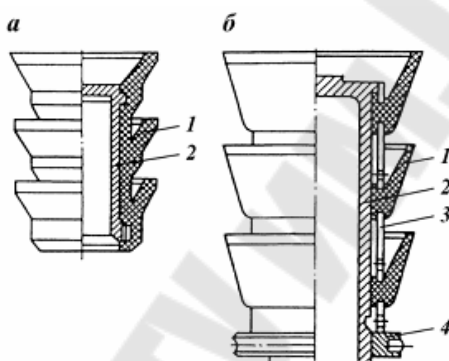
Пробки продавочные верхние типа ПП (а) и (б): а) – с пригуммированными манжетами; б) – с наборными резиновыми манжетами; 1 – резиновая манжета; 2 – алюминиевый корпус; 3 – дистанционная втулка; 4 – стяжная гайка
